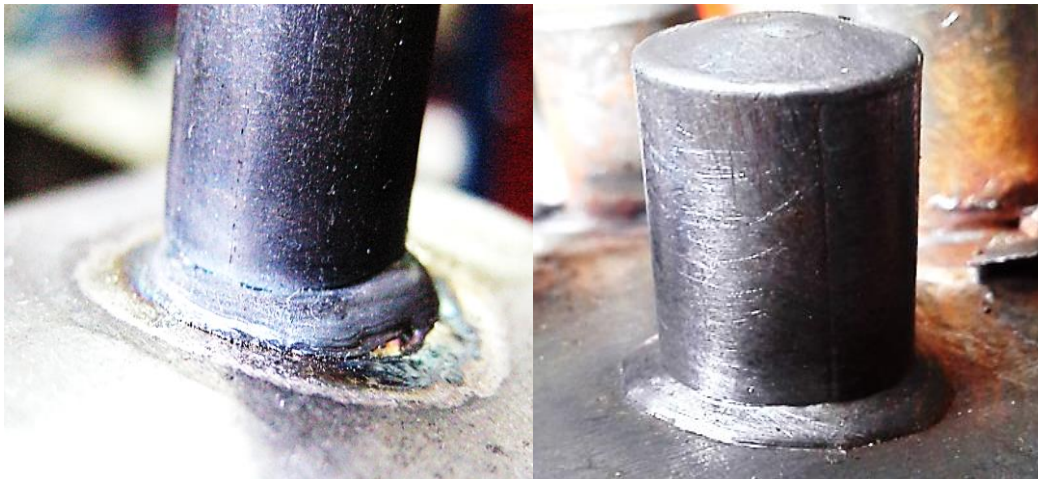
Фрагменти зварних з'єднань шип (сталь20) – труба (сталь 15X5M)
